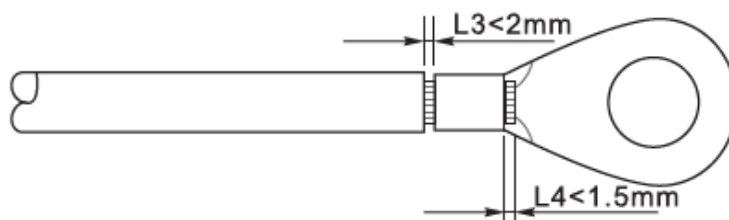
Przygotowanie przewodu uziemienia (1)
